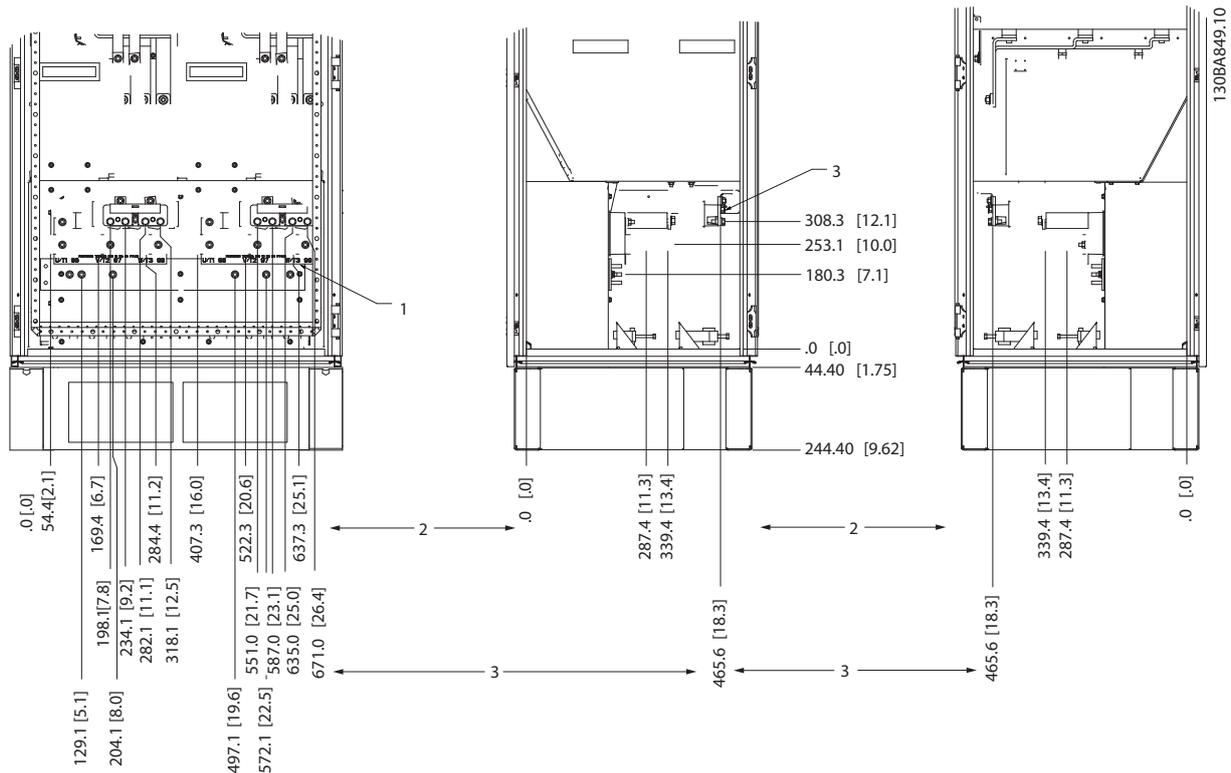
Klemmenpositionen – Wechselrichterschrank - F1 and F3 (Ansicht vorne, links und rechts). Die Kabelführungsplatte befindet sich 42 mm unterhalb des 0,0-Niveaus.
